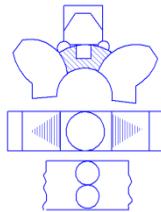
Установка шпилек по длине зуба с последующей их обваркой
